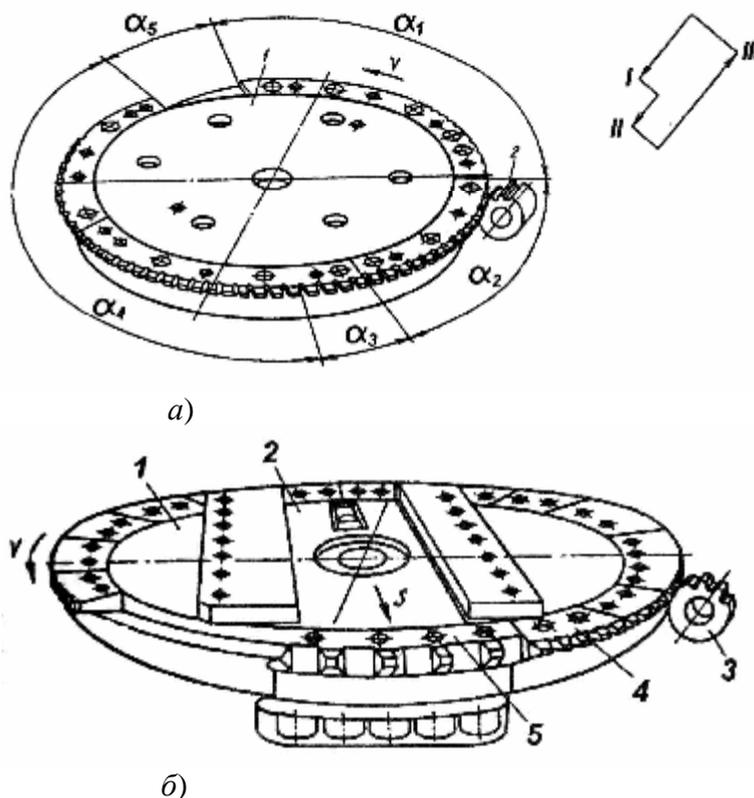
Инструменты для фрезепротягивания прямо-зубых и косозубых зубчатых колес (а): цикл 1 – черновое протягивание на всю глубину впадины; цикл 2 – завершение черновой протяжки при встречном фрезеровании; цикл 3 – чистовая обработка; цикл 4 – чистовое протягивание при попутной подаче заготовки; цикл 5 – поворот заготовки на один зуб; и для кругодиагонального протягивания зубчатых колес (б): 1 – корпус; 2 – ползун; 3 – заготовка; 4 – блок резцов черного протягивания; 5 – блок резцов (на ползуне) чистовой протяжки
